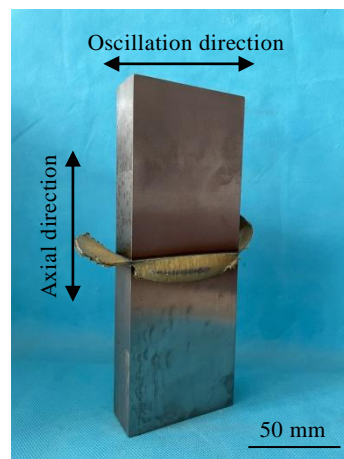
TC21 钛合金线性摩擦焊接头宏观形貌
